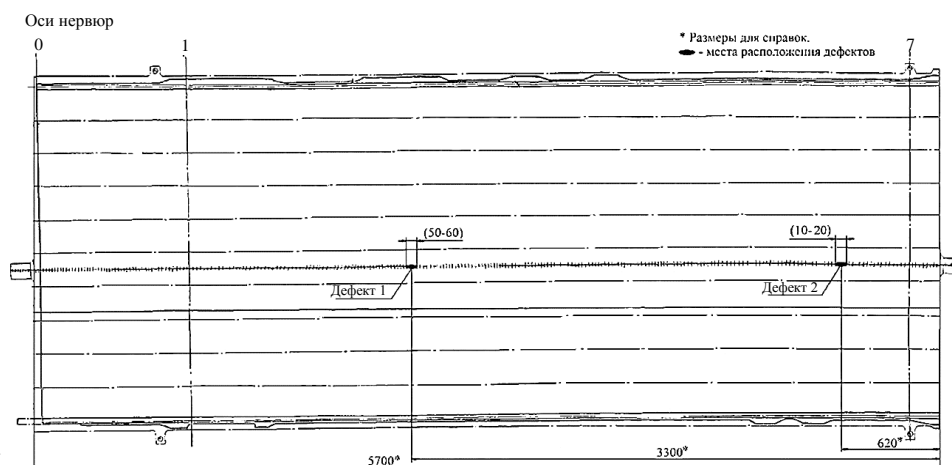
Эскиз сварной панели с местами доработки дефектов
